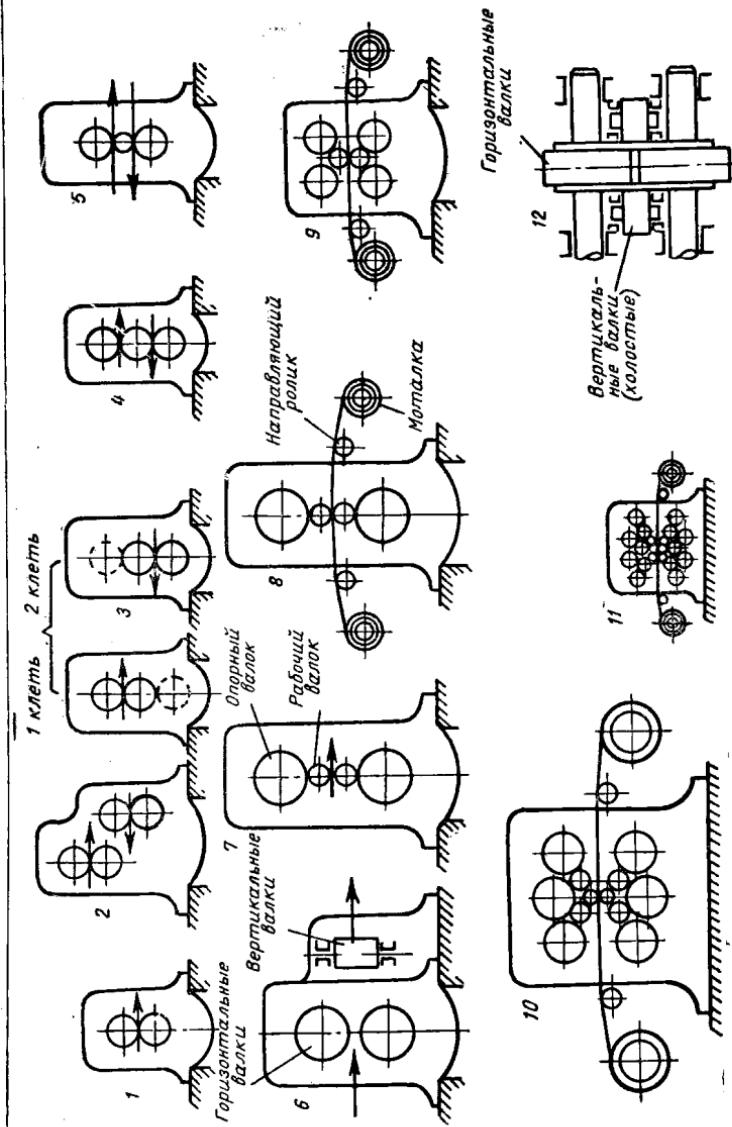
Расположение валков в рабочей клети прокатных станов:
